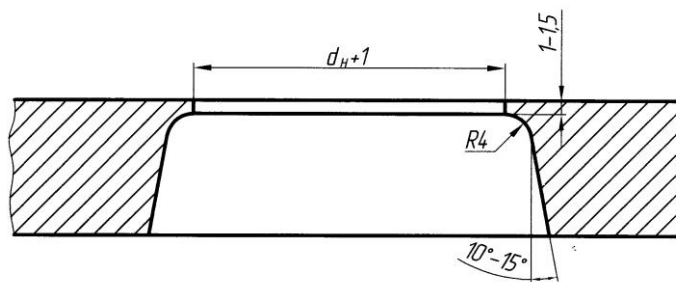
Подготовка кромок отверстий в нижней трубной решетке под приварку трубок
